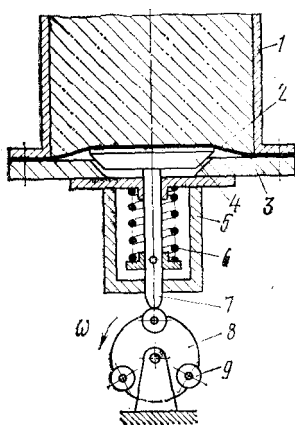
Схема формы с пульсаторами и дискороликовым возбуждением колебаний
